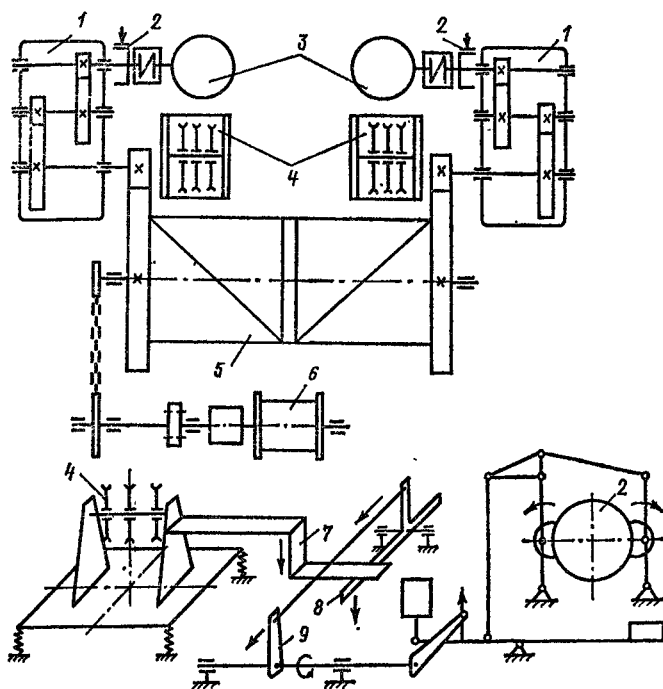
Схемы лебедки, защищенной от перегрузок, с расгор-
